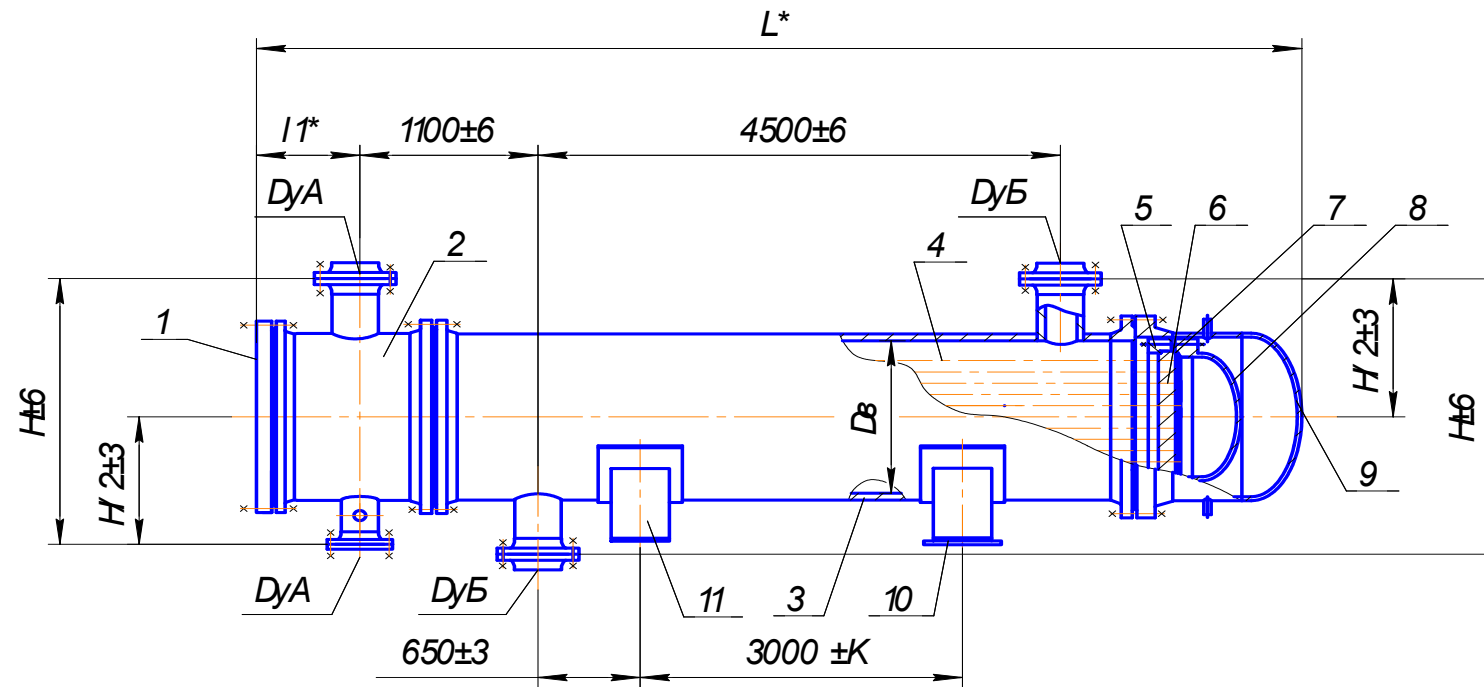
Аппарат типа КП. 1 – крышка камера распределительной; 2 – камера распределительная; 3 – кожух; 4 – труба теплообменная; 5 – полукольцо; 6 – решетка трубная подвижная; 7 – прокладка плавающей головки; 8 – крышка плавающей головки; 9 – крышка кожуха; 10 – опора подвижная; 11 – опора неподвижная.
